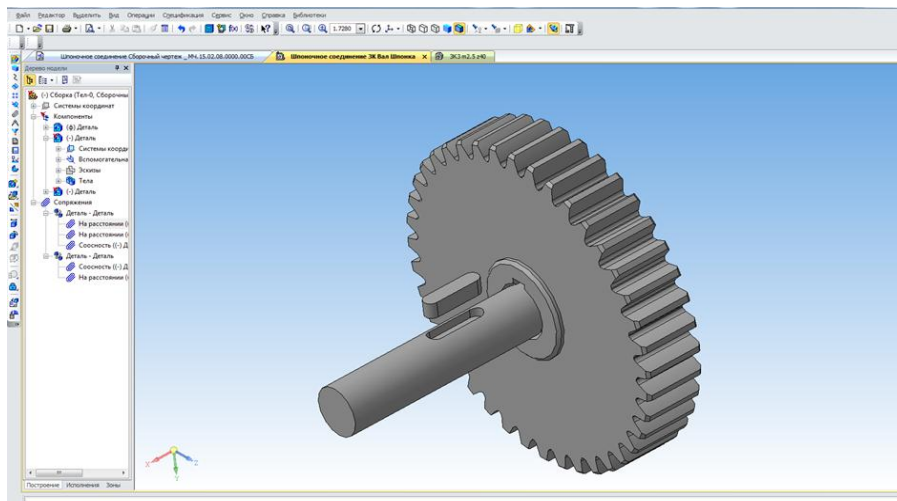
Демонстрация зубчатого колеса, вала и шпонки в КОМПАС
